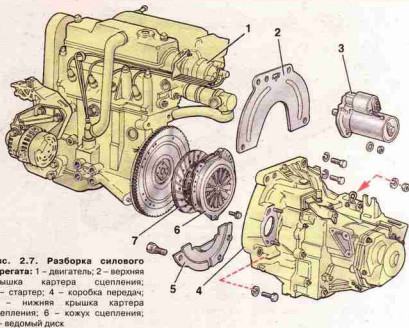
Разборка силового агрегата: 1 – двигатель; 2 – верхняя крышка картера сцепления; 3 – стартер; 4 – коробка передач; 5 – нижняя крышка картера сцепления; 6 – кожух ведомый диск; 7 – ведомый диск
